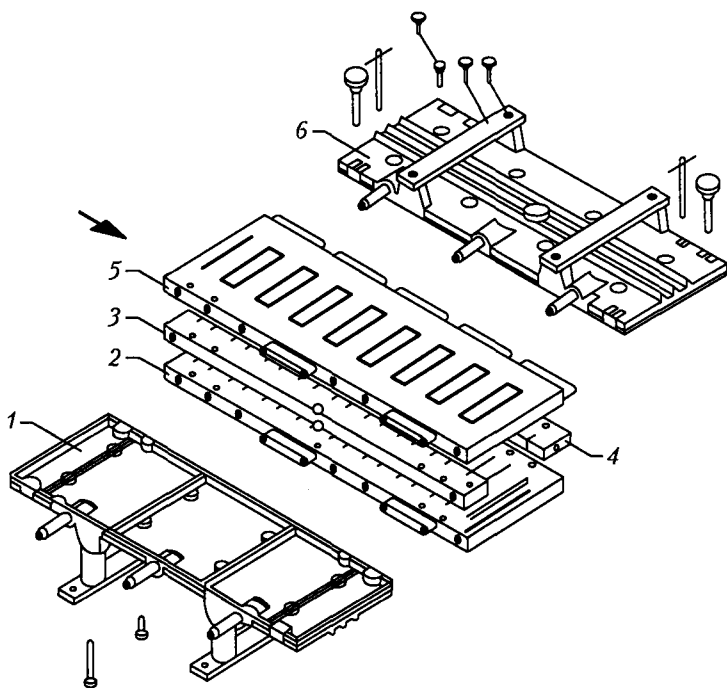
Детали длинномерного вакуумного калибратора:
